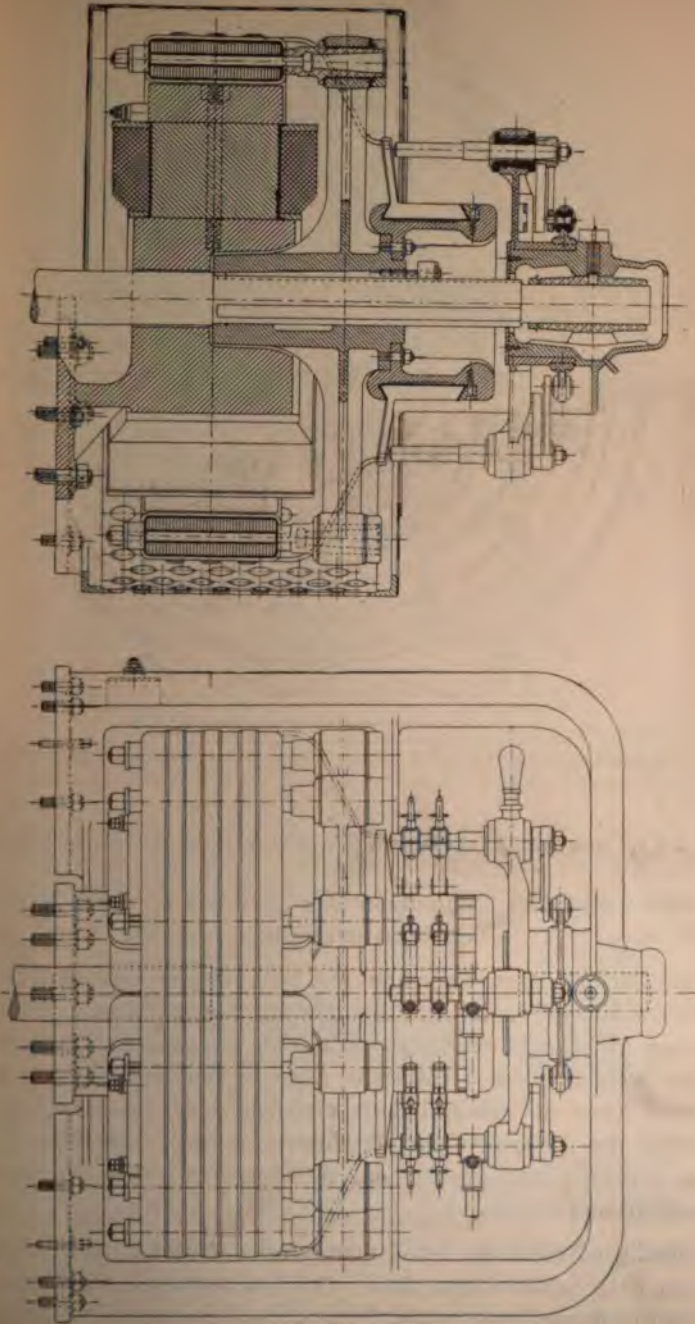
b* und *c*. Siemens & Halske: Innenpolmaschine.
